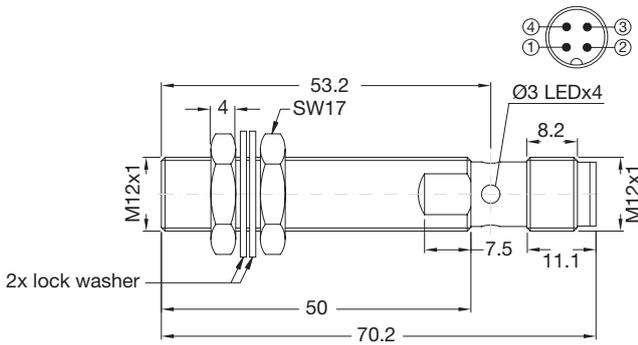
Lange Ausführung, bündiger Einbau, Steckversion
